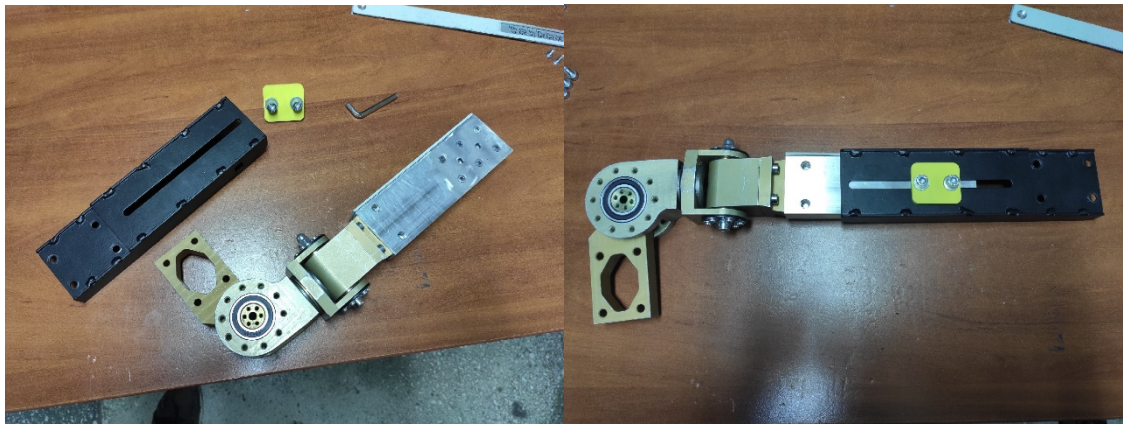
Соединение профиля бедра и корпуса бедра регулировочным креплением
